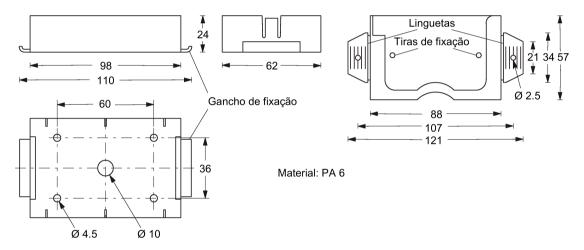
Desenho de dimensões do espaçador 6GT2190-0AA00 com bolsa de fixação 6GT2190-0AB00
